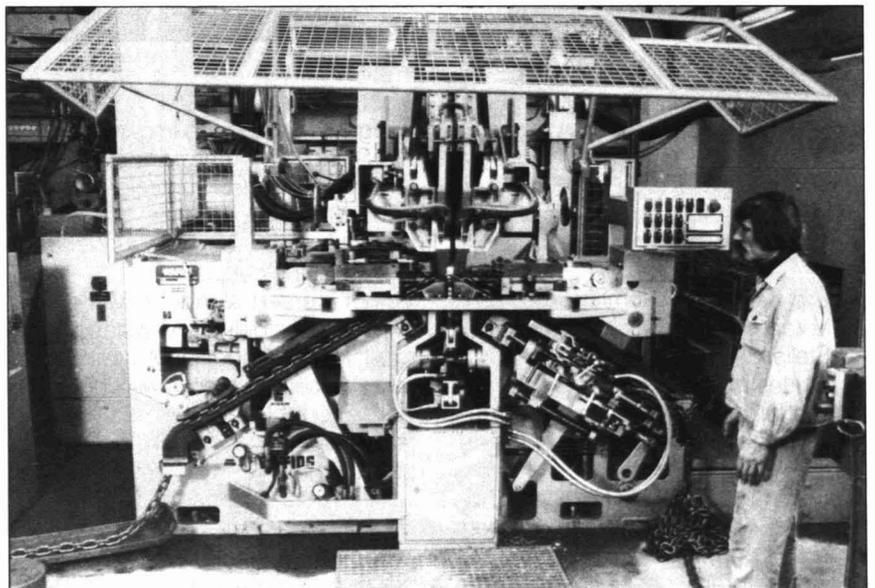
Mikroprozessorgesteuerter Kettenschweißvollautomat
